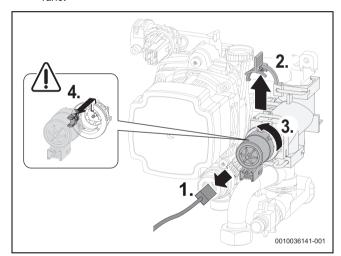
Separar el motor de la válvula de 3 vías (variante sin tornillos)
